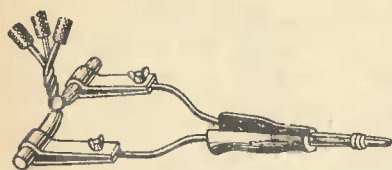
Клещи для сварки алюминиевых жил проводов.
